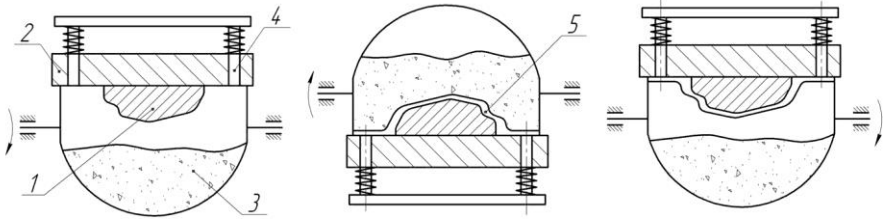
Схема виготовлення оболонкової форми:
